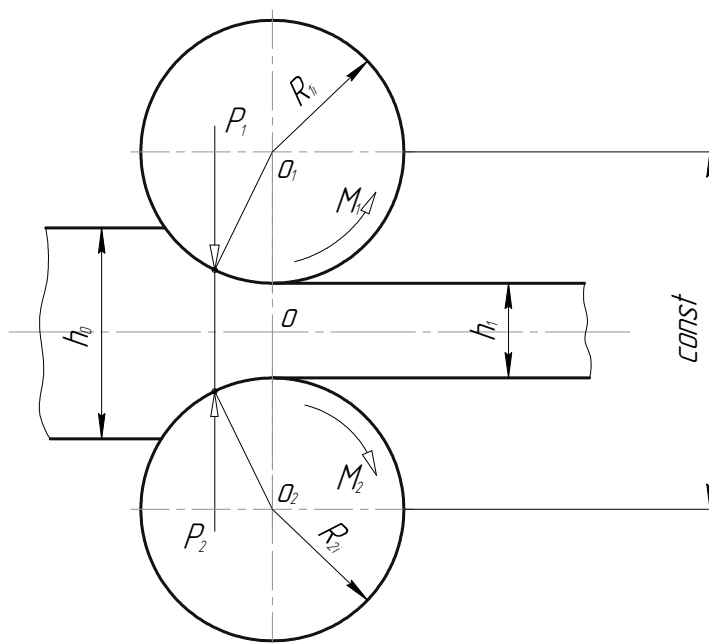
Схема прокатки одного элемента пера лопатки ГТД
